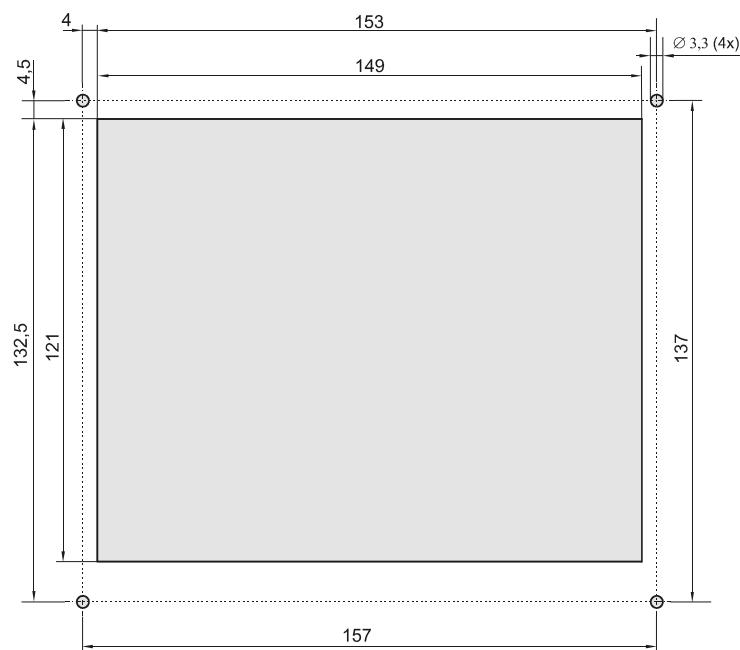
Lochmaske der LCD 19 für Frontplattenausschnitt
